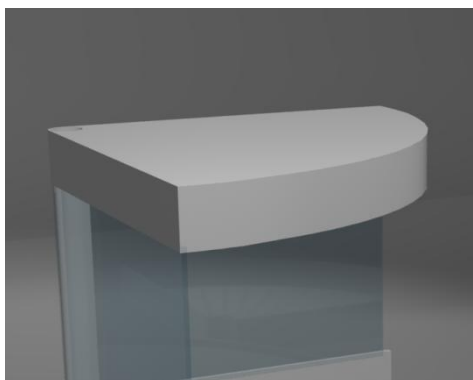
Крышка размещения фитолампы и знакового индикатора
